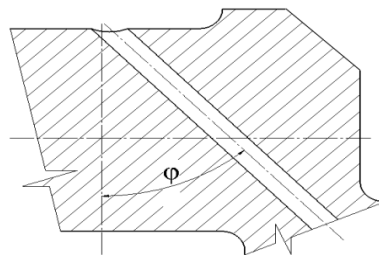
Úpravy vyústění mazacího otvoru, upraveno [1]
